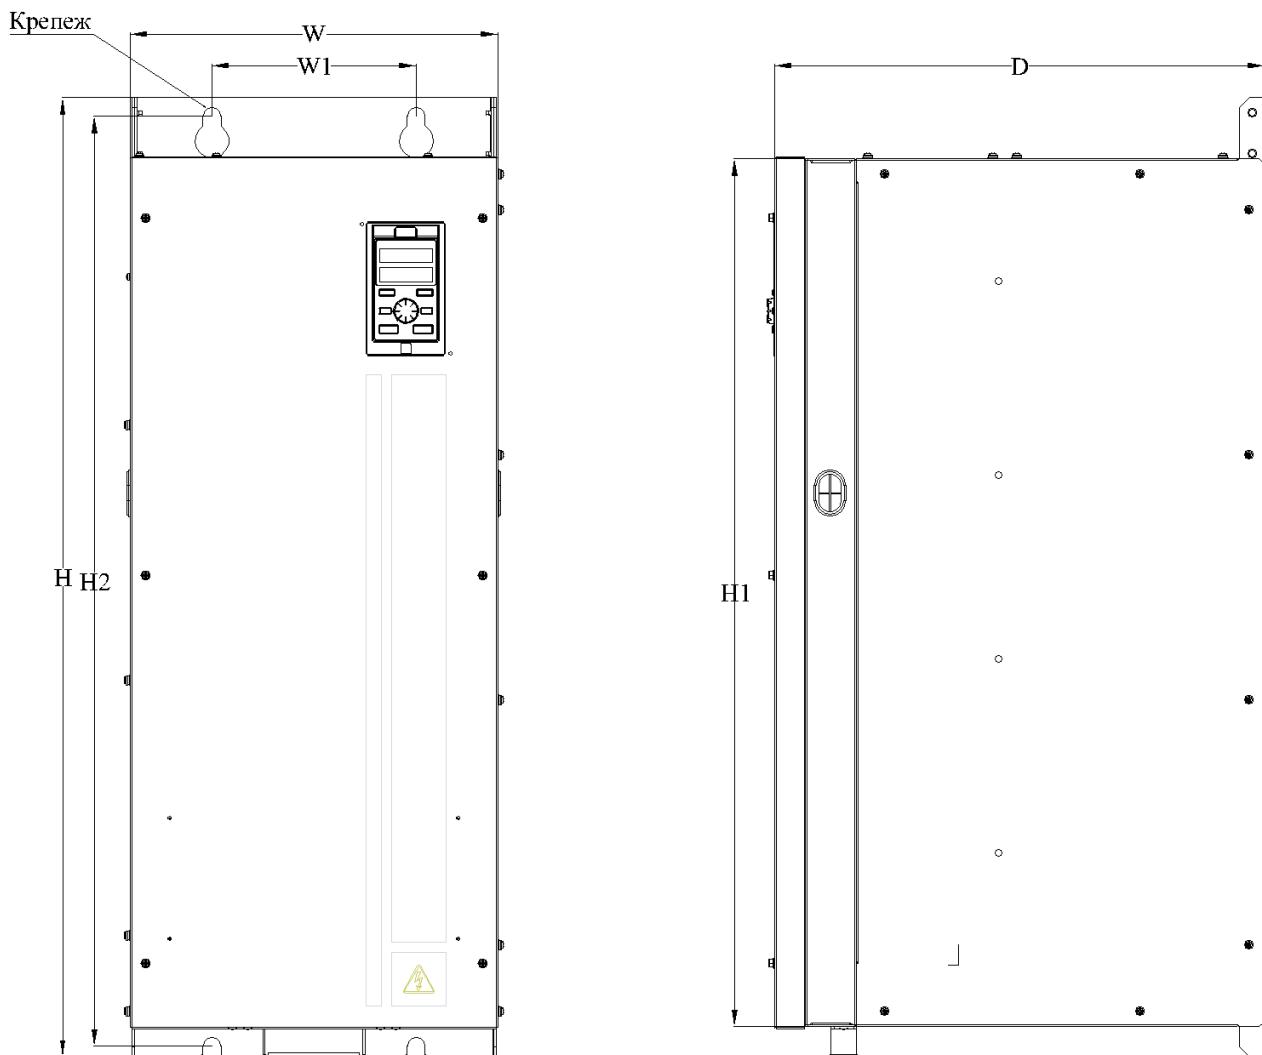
Чертеж преобразователя частоты типоразмер 8
